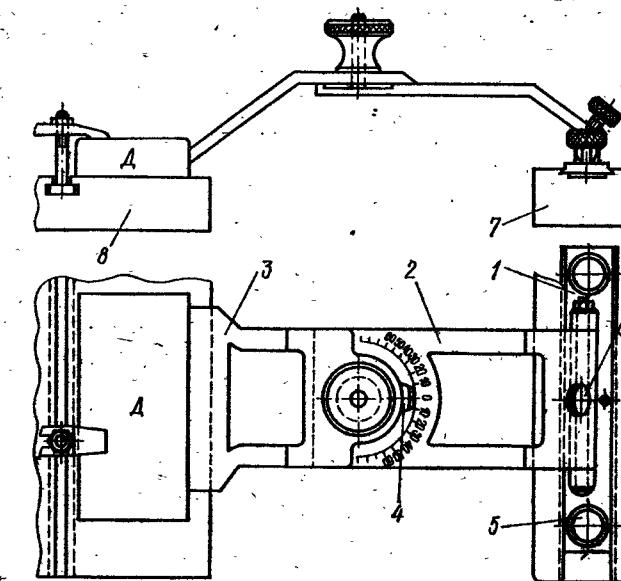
Универсальное приспособление для точной установки деталей на станке-пантографе
